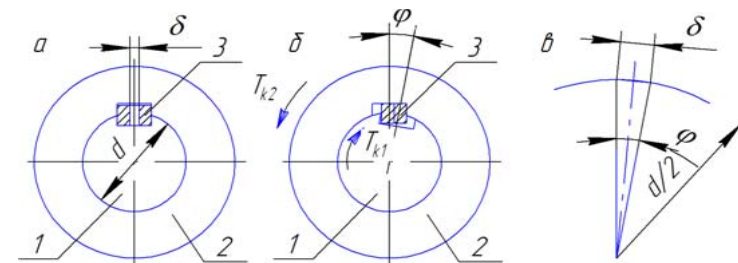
Схеми роботи з'єднання типу "вал-маточина" з пружною призматичною шпонкою:
